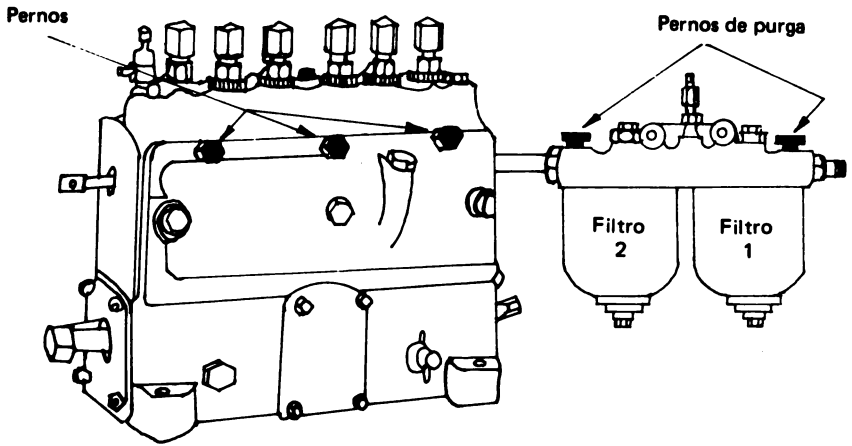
Desatornille 1 ó 2 vueltas los pernos de purga de un motor Diesel (filtros y bomba).
